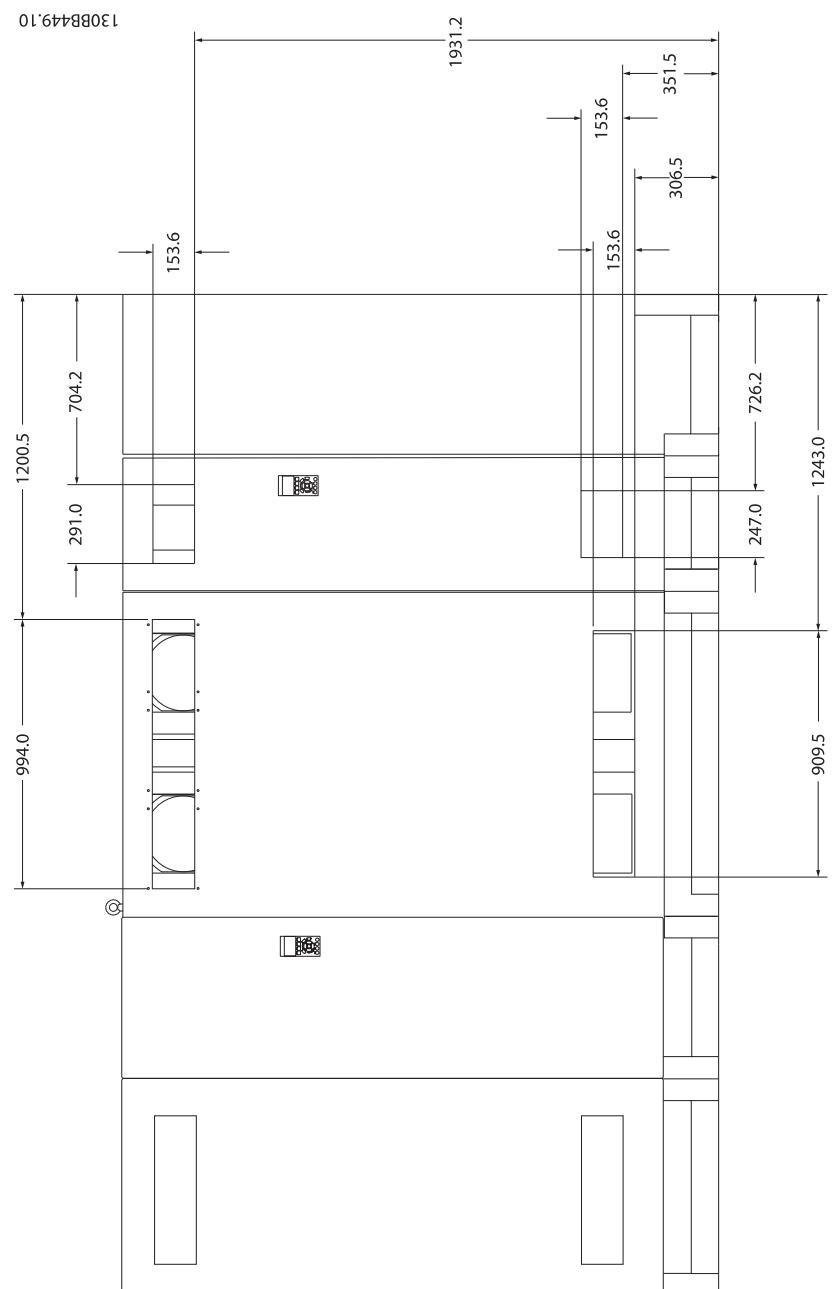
Типоразмер корпуса F17, вид сзади
